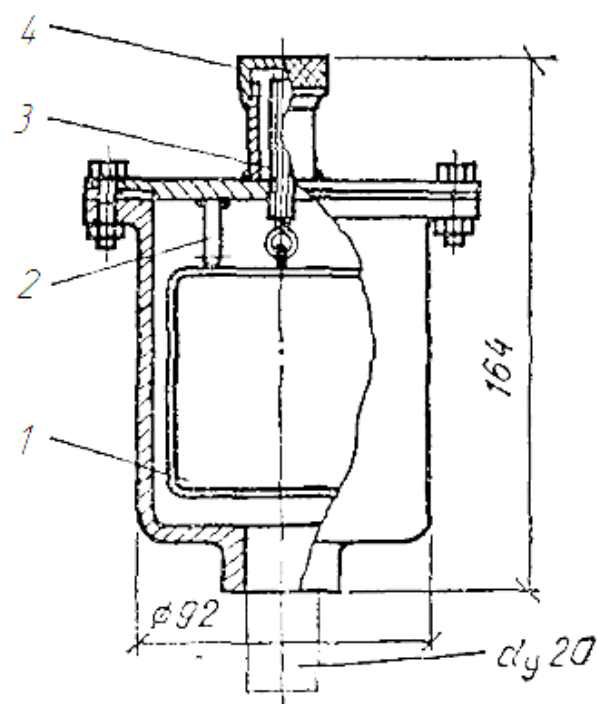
Автоматический воздухоотводчик: 7 – поплавок; 8 – упор; 9 – пружинный клапан, 10 – защитный колпак
